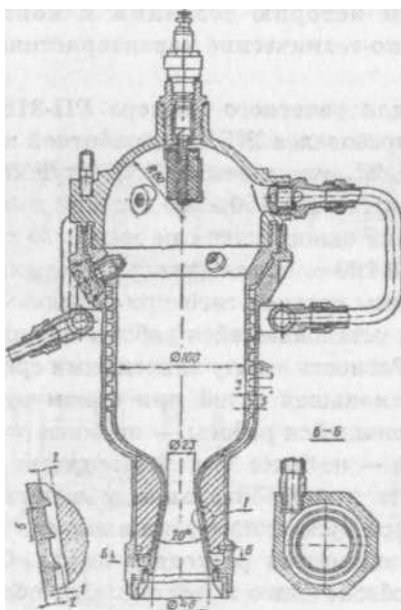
Жидкостный ракетный двигатель ОРМ-65 [12]
